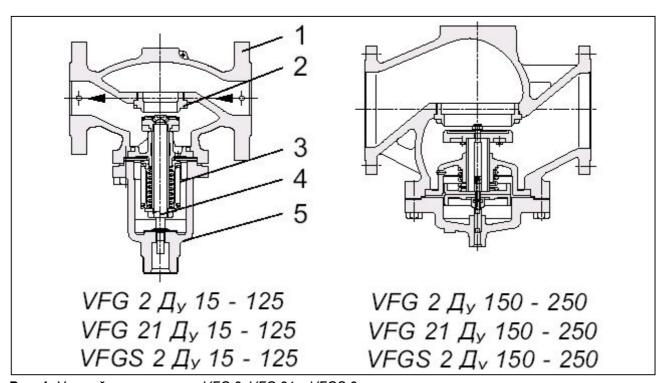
Устройство клапанов VFG 2, VFG 21 и VFGS 2.* 1 – корпус клапана; 2 – седло клапана; 3 – сильфон; 4 – золотник; 5 – крышка.
